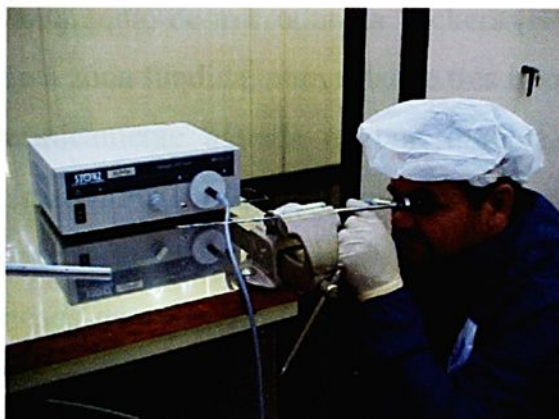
Inspeção de um corpo-de-prova soldado
